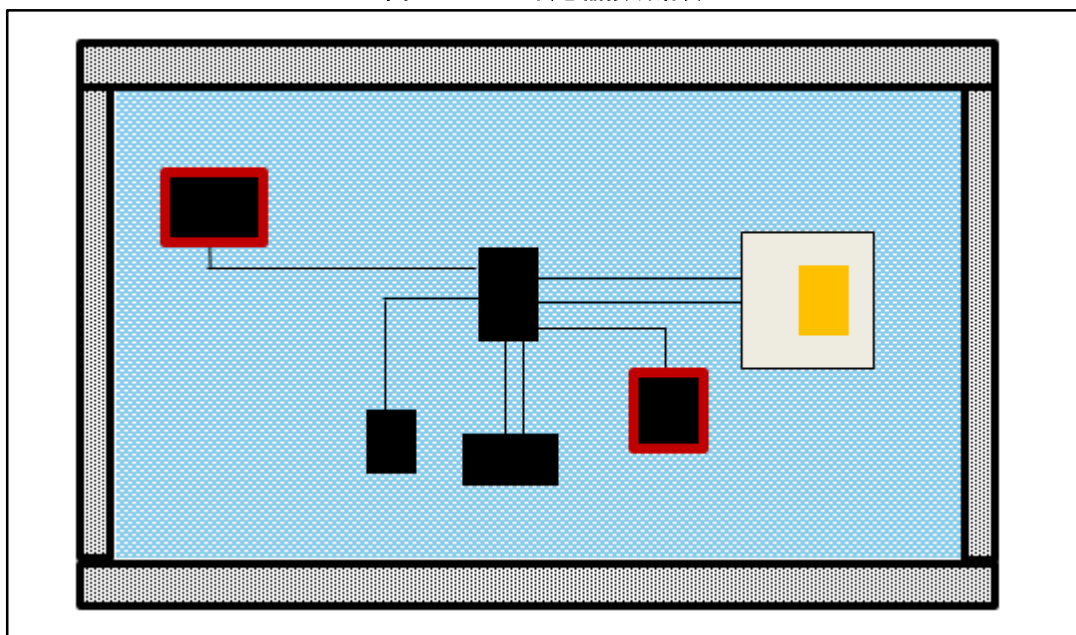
“PCB 上传感器接线不良”采用了错误的金属线尺寸。导线的尺寸越大, 热传导水平越高。
